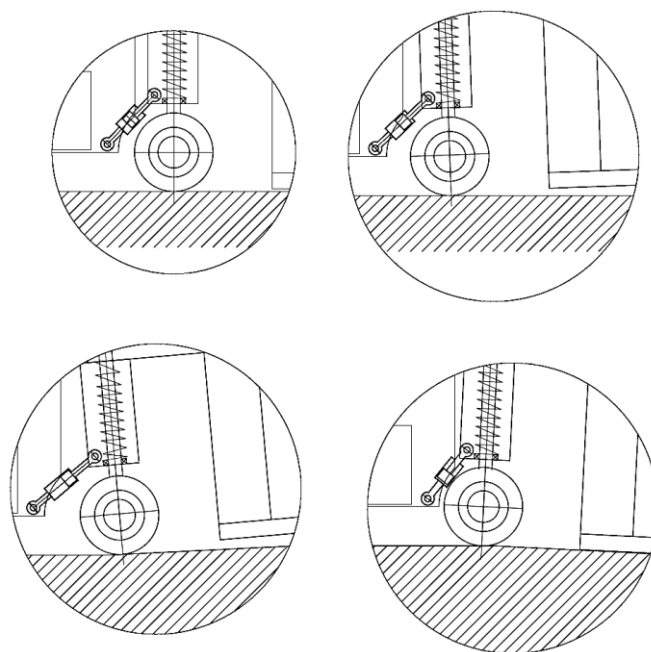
Pormenores de instalação de cilindros hidráulicos para elevação da estrutura principal do *Stacker*.
